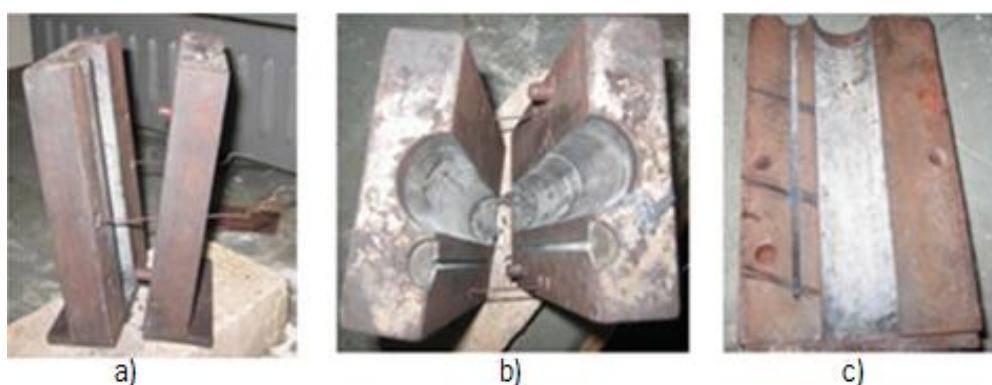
Coquilha utilizada no fabrico das varetas: a) Vista lateral; b) Vista de topo; c) Canais de escape
